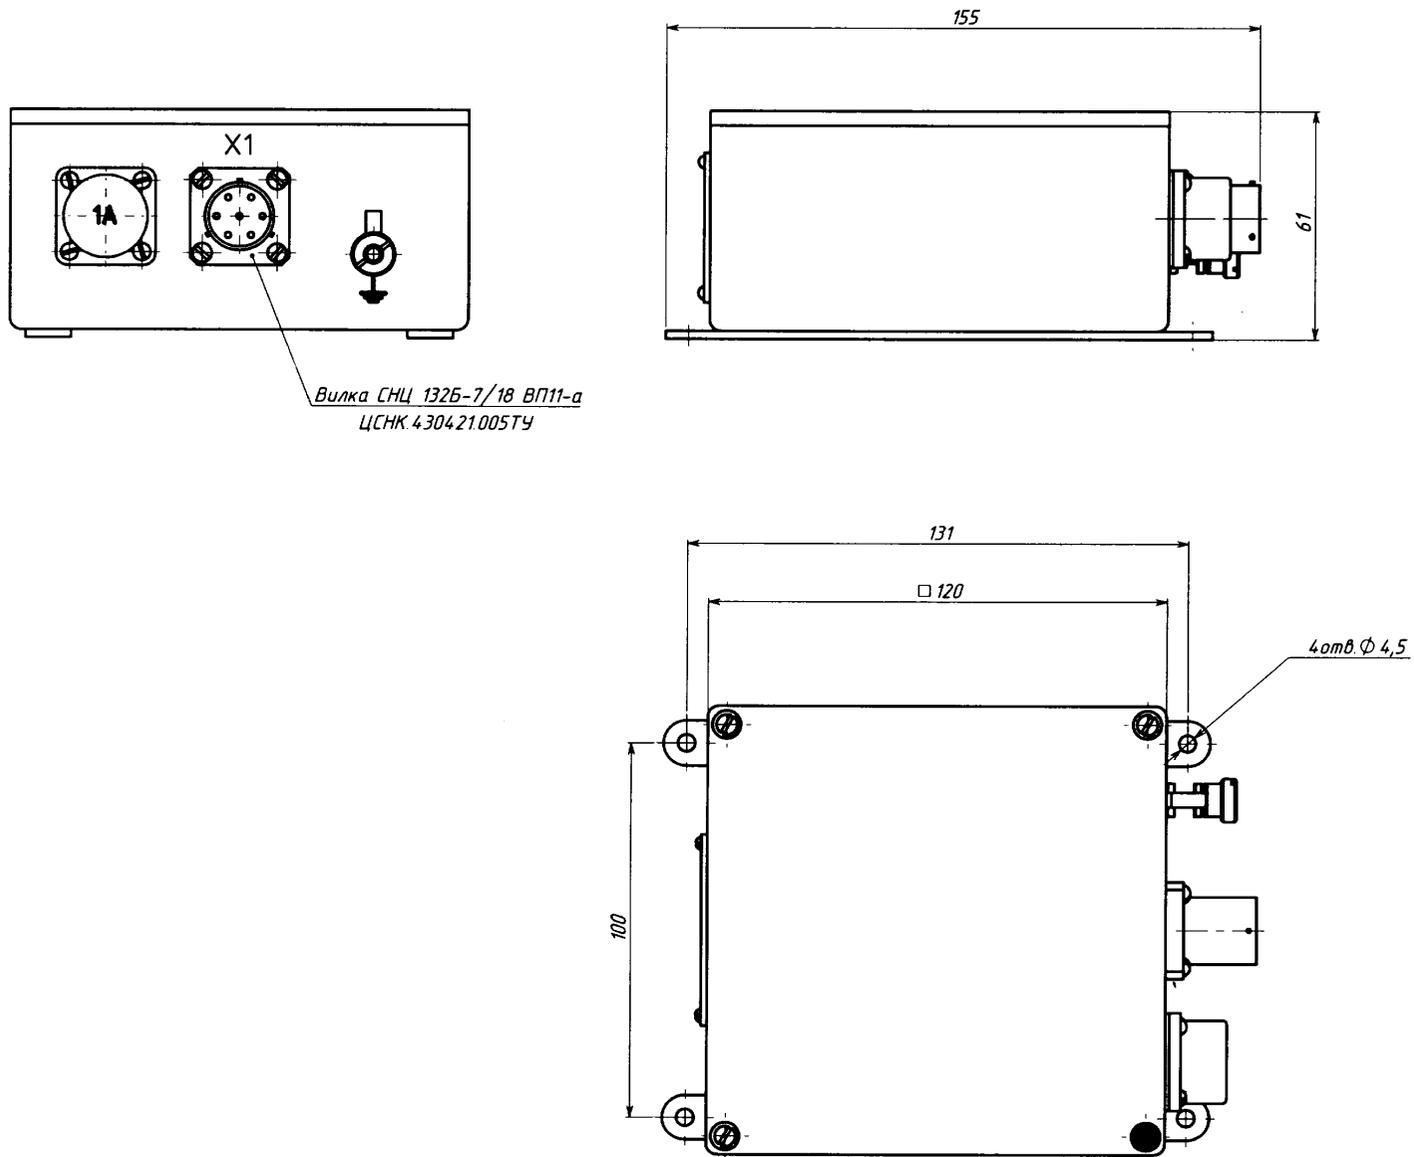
Габаритные и присоединительные размеры блока питания токового датчика БПТД (БПТД-1)
